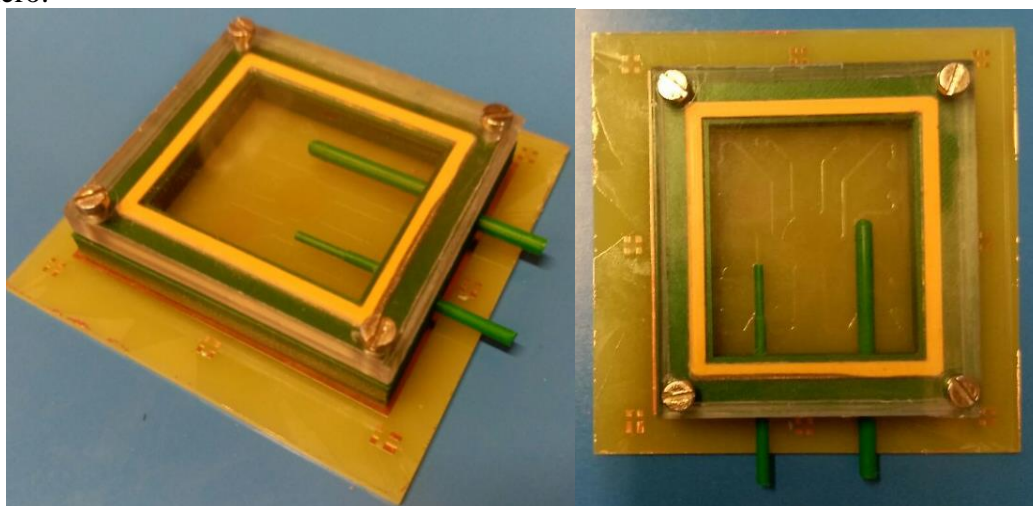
Molde para PDMS. Diseñado y fabricado por el GM-US.
